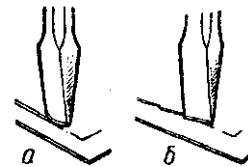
Зубила з заокругленими (а) і прямими (б) лезами
